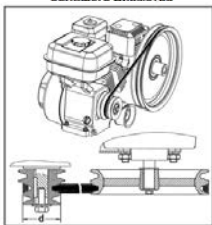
Установка ремня в ручей шкива меньшего диаметра
